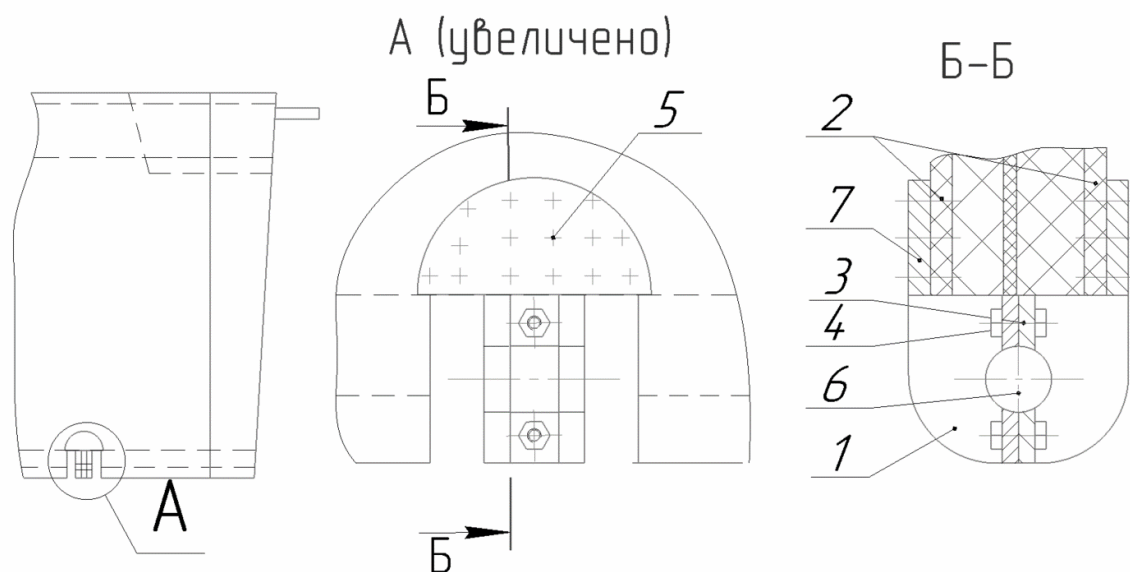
Шарнирная опора Б: 1 – композитная петля; 2 – стенки композитного борта; 3 – шпилька; 4 – гайка; 5 – КЭ; 6 – палец; 7 – металлическая пластина
